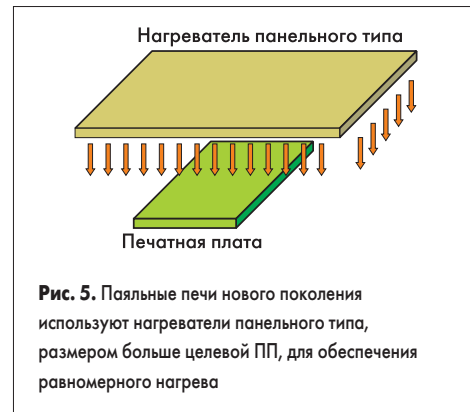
Паяльные печи нового поколения используют нагреватели панельного типа, размером больше целевой ПП, для обеспечения равномерного нагрева
